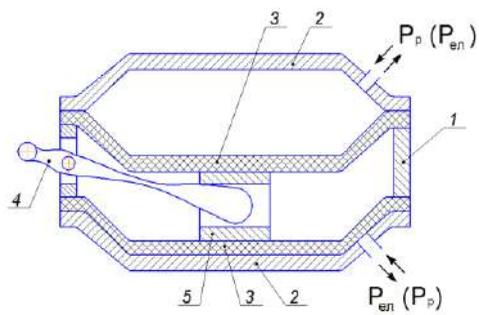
Мембранный поворотный гидродвигун:
